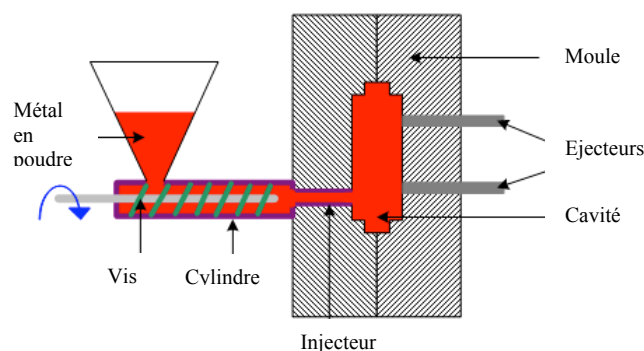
Schéma de principe du procédé de moulage par injection de métal en poudre
